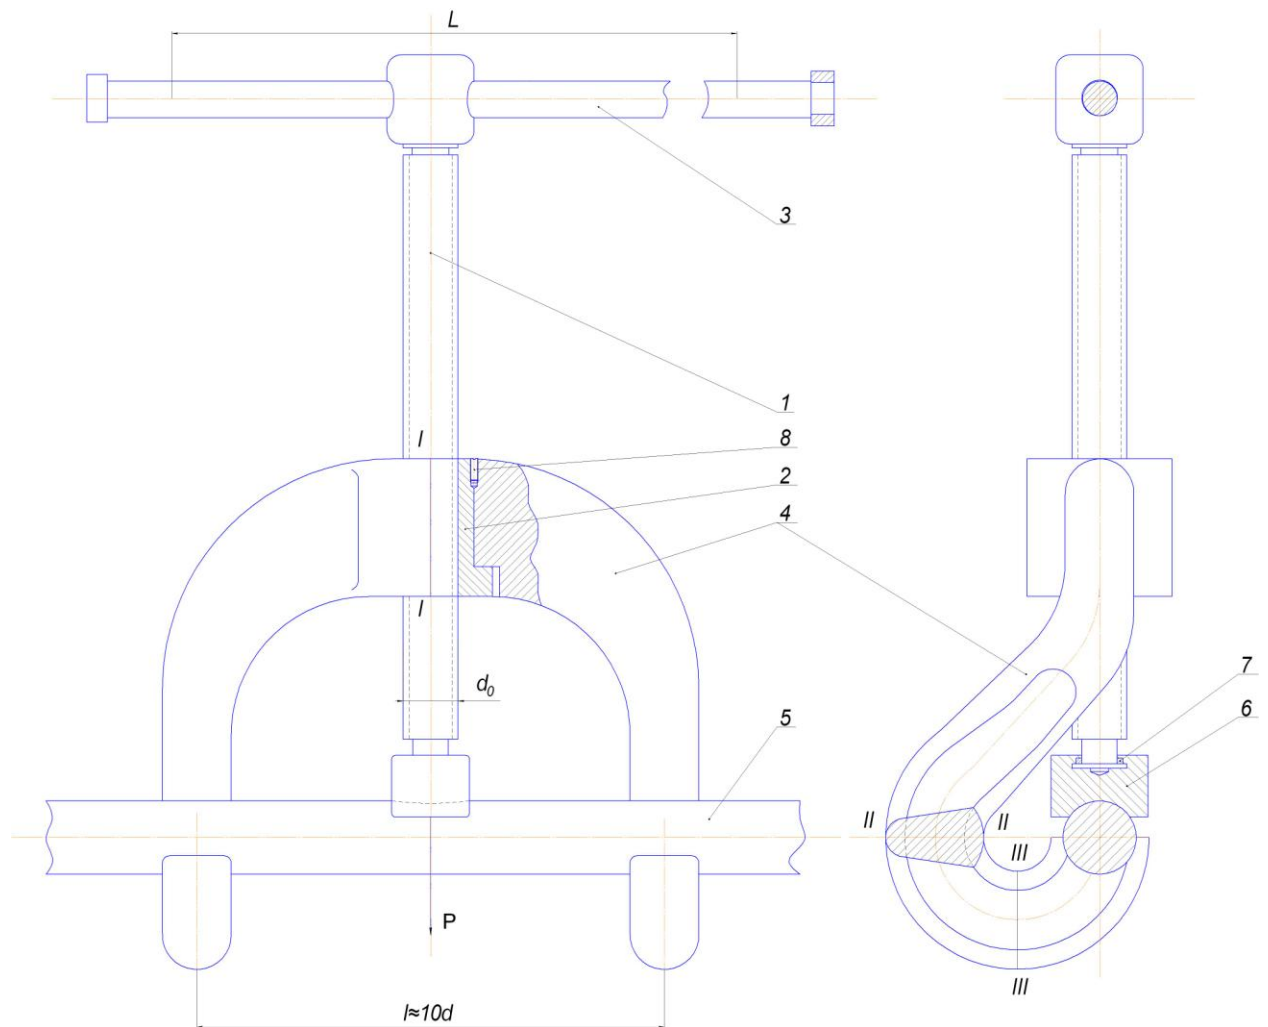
Монтажное приспособление для изгиба арматурных прутков: 1 – винт; 2 – гайка; 3 – рукоятка; 4 – скоба; 5 – пруток; 6 – оправка; 7 – штифты; 8 – крепежный винт.
